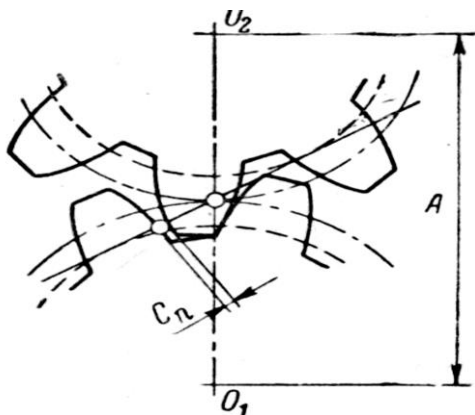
Боковой зазор между зубьями зацепляющихся колес
